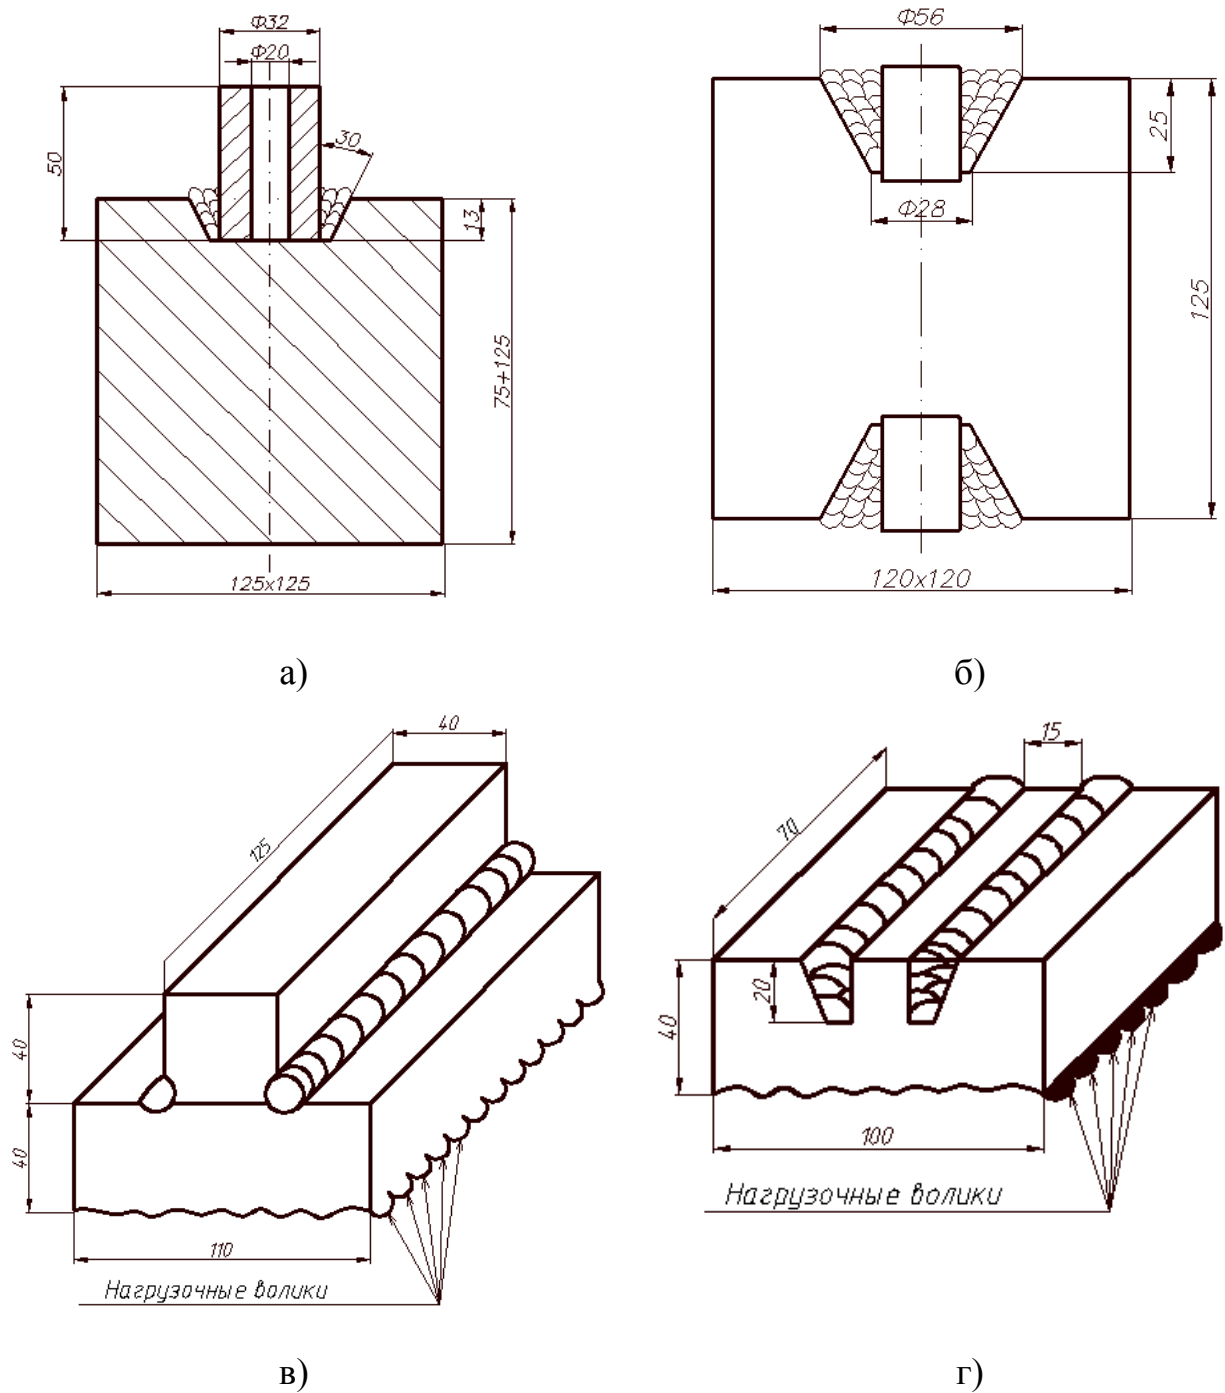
Сварные образцы для технологических испытаний склонности к ЛРОЗ: а – проба BWRA; б – проба ЦНИИТМАШ; в – тавровая проба ЦНИИМС; г – стыковая проба ЦКТИ
